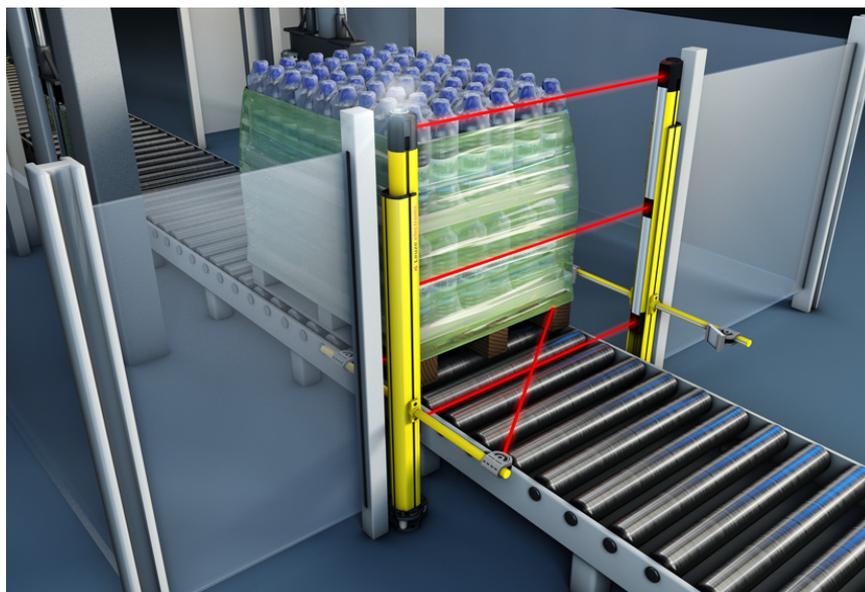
Protezione di accesso con muting temporale a 2 sensori per un'applicazione con avvolgipallet
